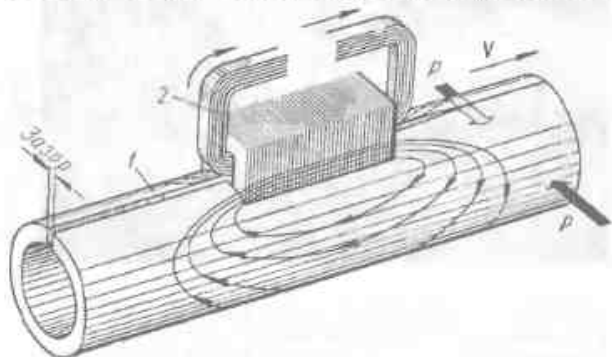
Мгновенное направление вихревых токов при индукционной сварке продольным швом ( $v$  — скорость сварки)
